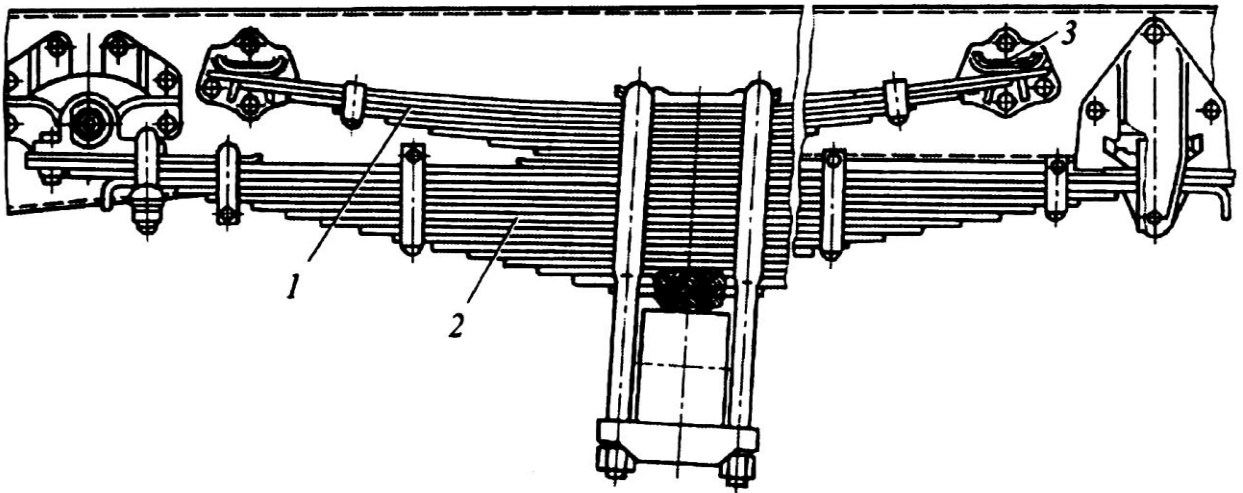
Ресорна підвіска з додатковою ресорною:
